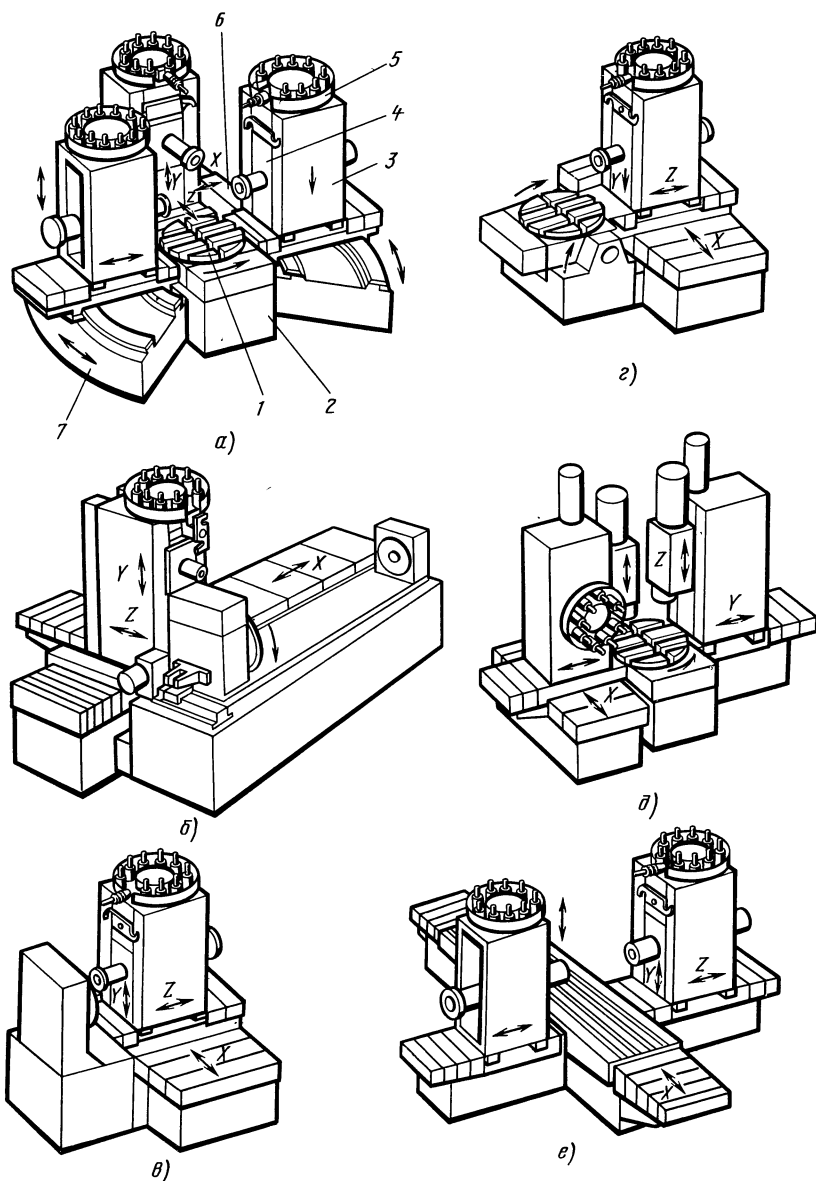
Компоновки агрегатных станков с ЧПУ:
